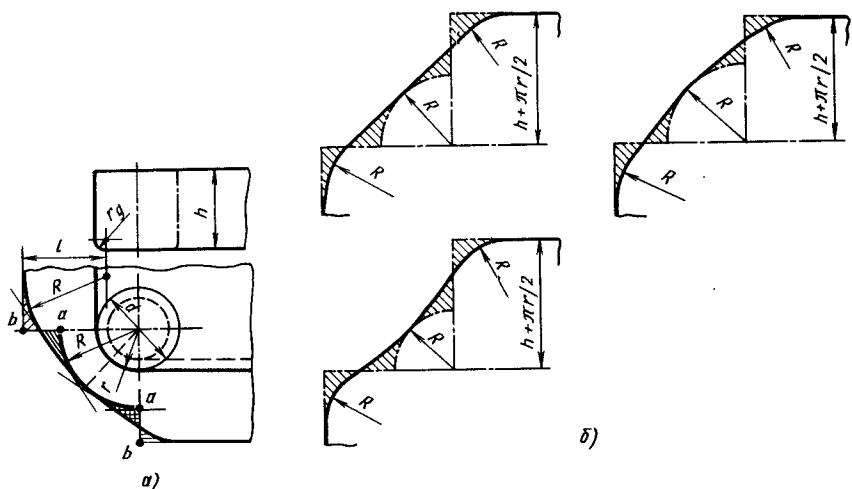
Построение контура заготовки: а — пример построения; б — возможные варианты оформления скруглений в углах заготовки
